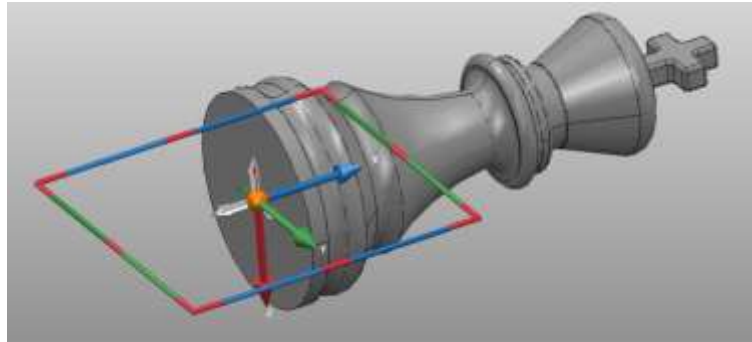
Система координат для чорнового фрезерування другої половини деталі
